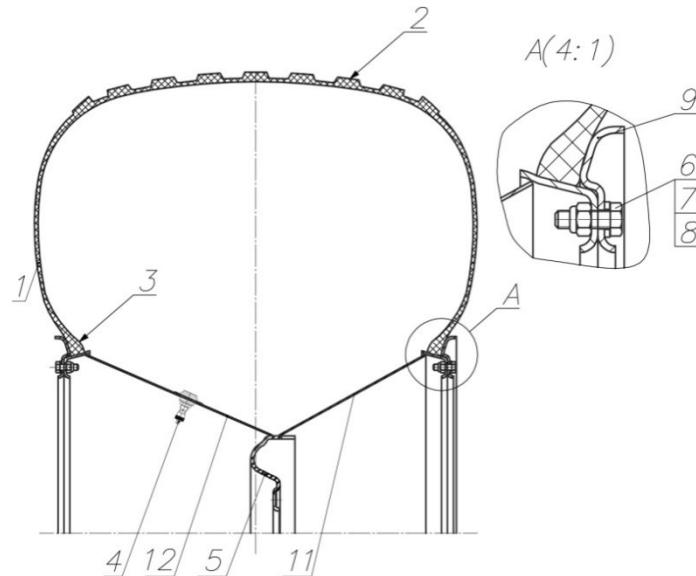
Шина 1300x600-533 ТРЭКОЛ с колесом в сборе
